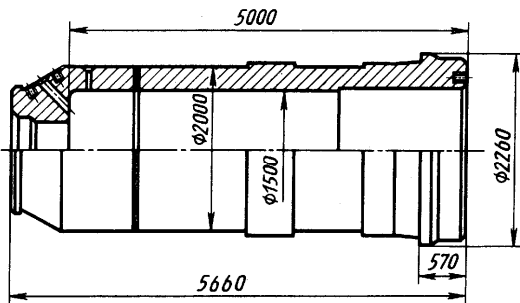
Сварно-кованый цилиндр крупного прессы
